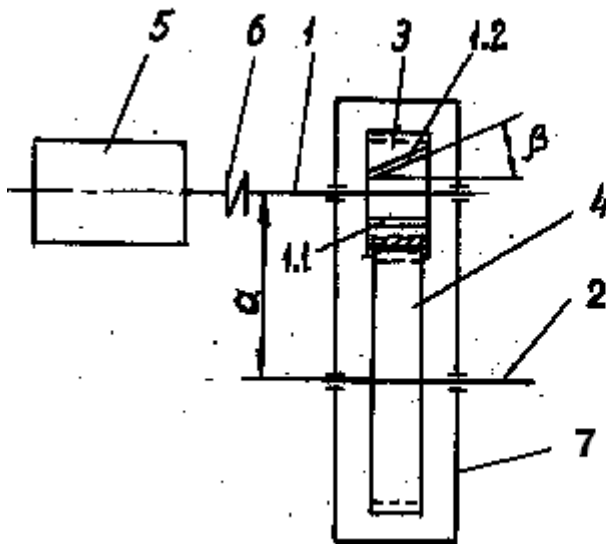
Кинематическая схема привода: 1 – ведущий вал, 2 – ведомый вал, 3 – шестерня, 4 – зубчатое колесо, 5 – электродвигатель, 6 – упругая муфта, 7 – корпус .
